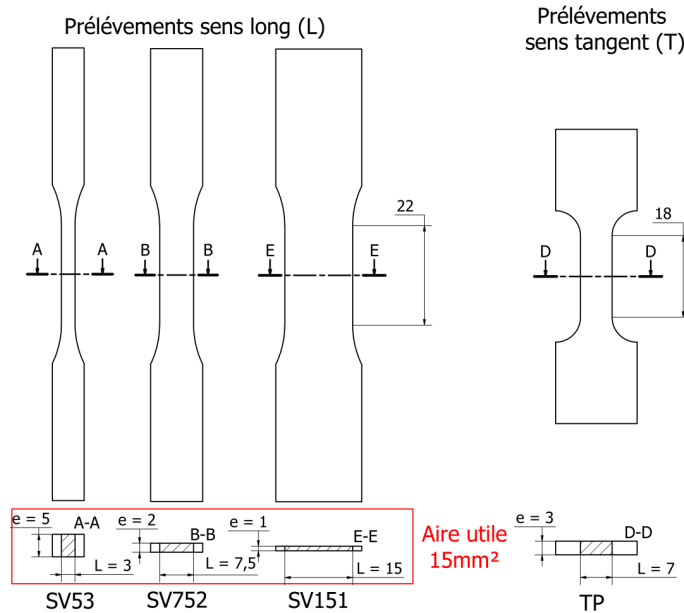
Géométrie des éprouvettes à Section Variable (SV) et de Traction Plane (TP) - dimensions en millimètres
